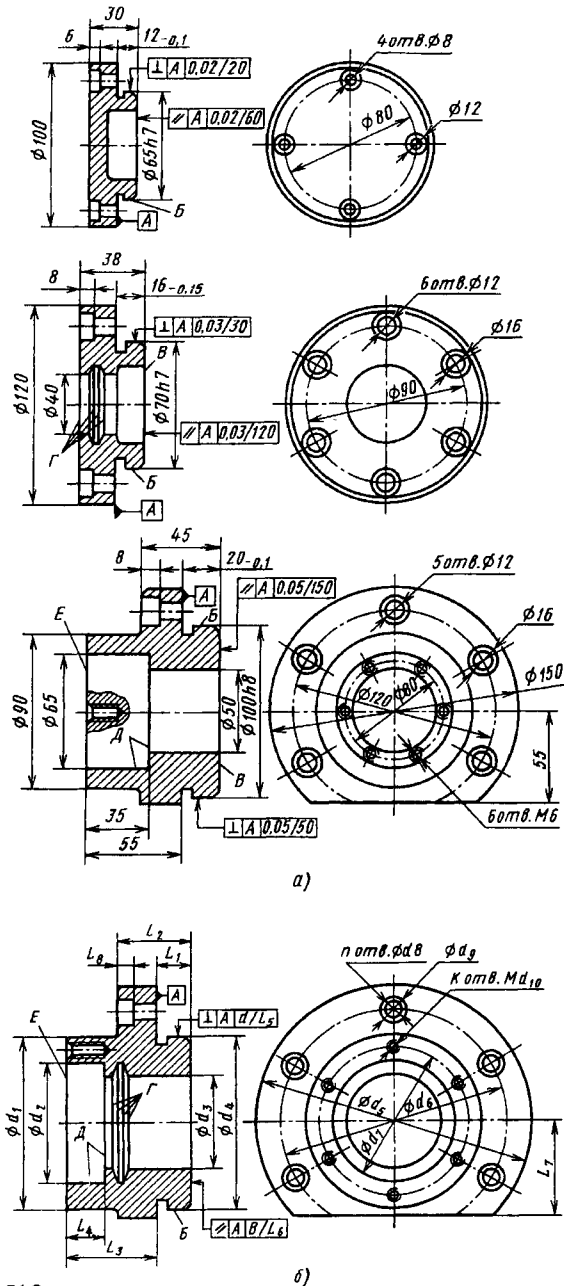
Представители класса фланцев (а) и типовая деталь (б)
